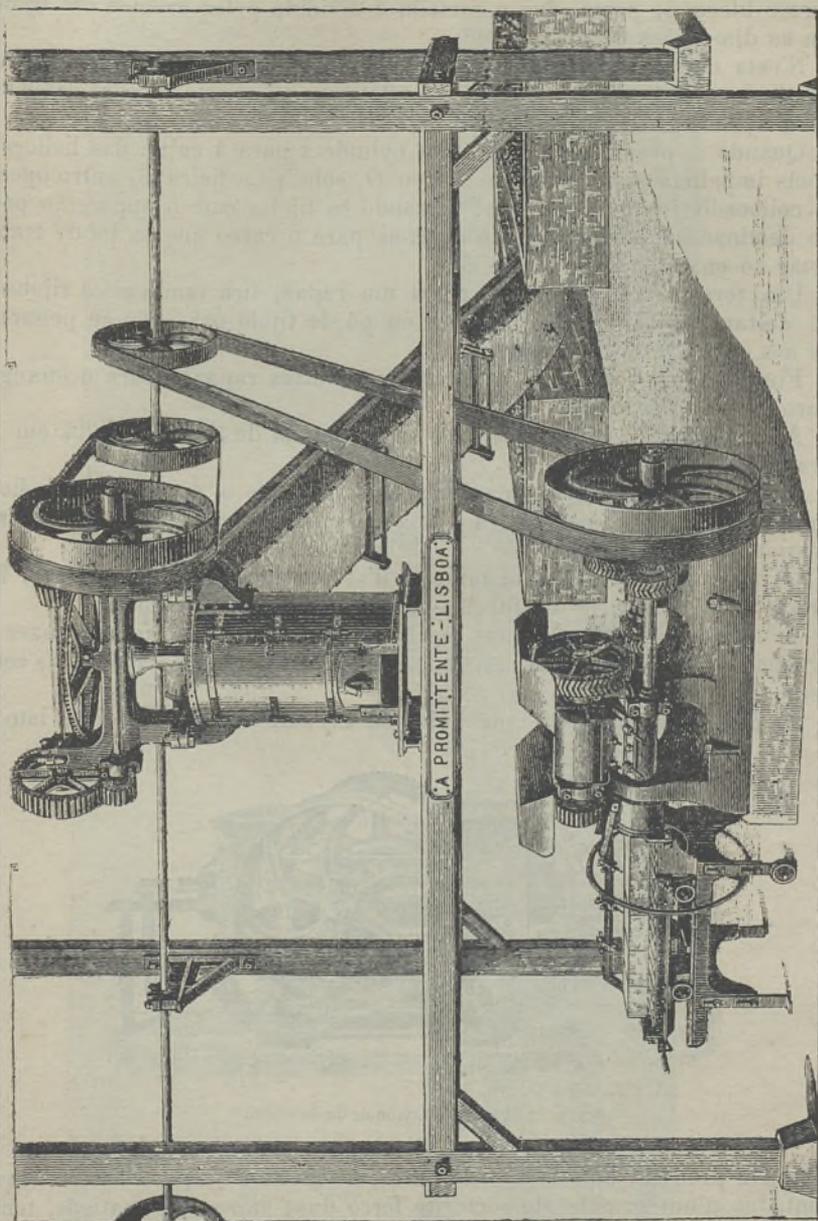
Instalação das machinas para o fabrico mecanico de fiçolo
